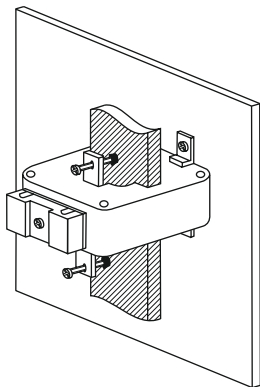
Установка трансформаторов ТШП-0,66 габаритов 30, 30Т, 40, 60 на шине при помощи крепежной пластины и винтов
